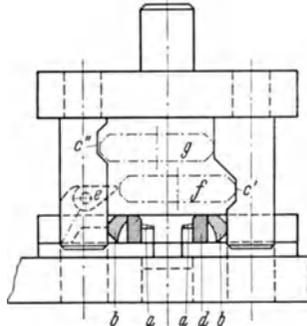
Werkzeug zum Lochen einer Kapsel am zylindrischen Teil.
